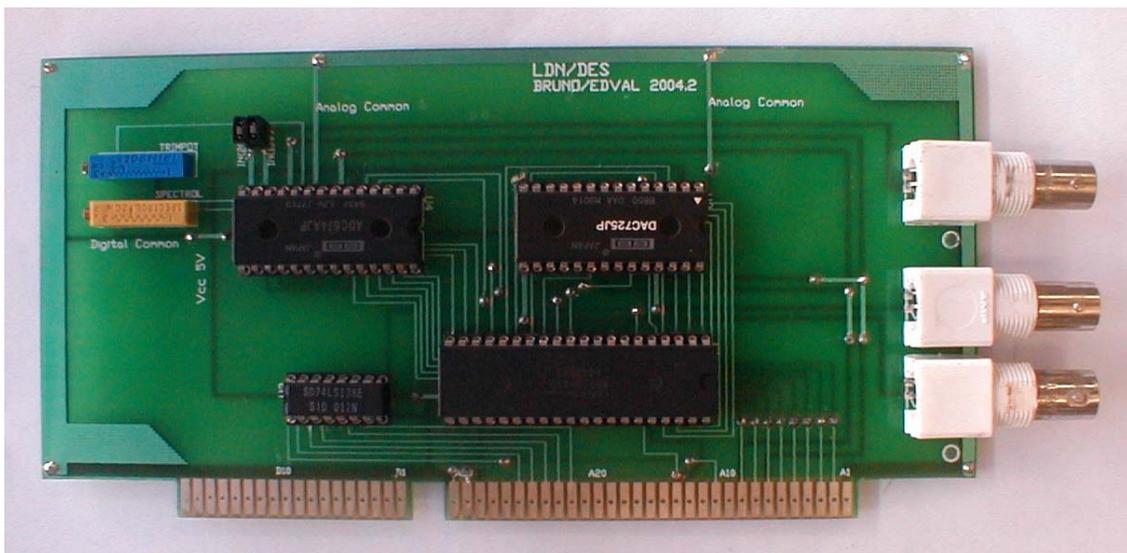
Placa de aquisição em circuito impresso após finalizada a montagem.
